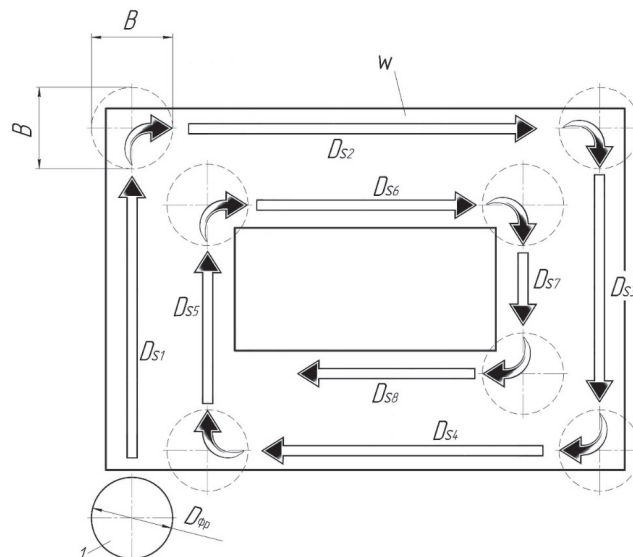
Схема фрезерування однією торцевою фрезою: 1 – торцева фреза; W – заготовка; $D_{\text{фр}}$ – діаметр фрези; B – максимально можлива ширина фрезерування; D_{S1} , D_{S2} , D_{S3} , D_{S4} , D_{S5} , D_{S6} , D_{S7} , D_{S8} – напрямки подачі
